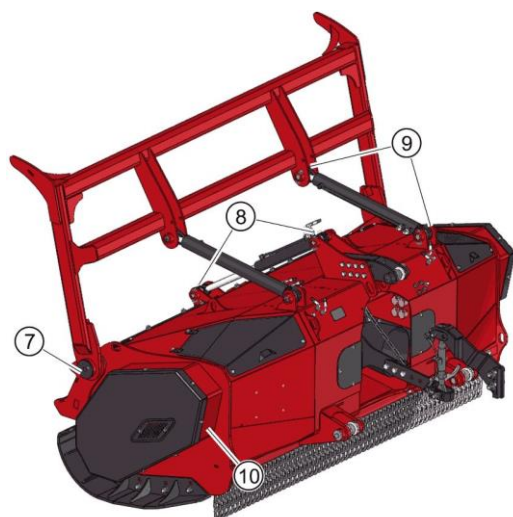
Точки смазки заслонки системы дополнительного измельчения, устройства прижима и ременного привода
